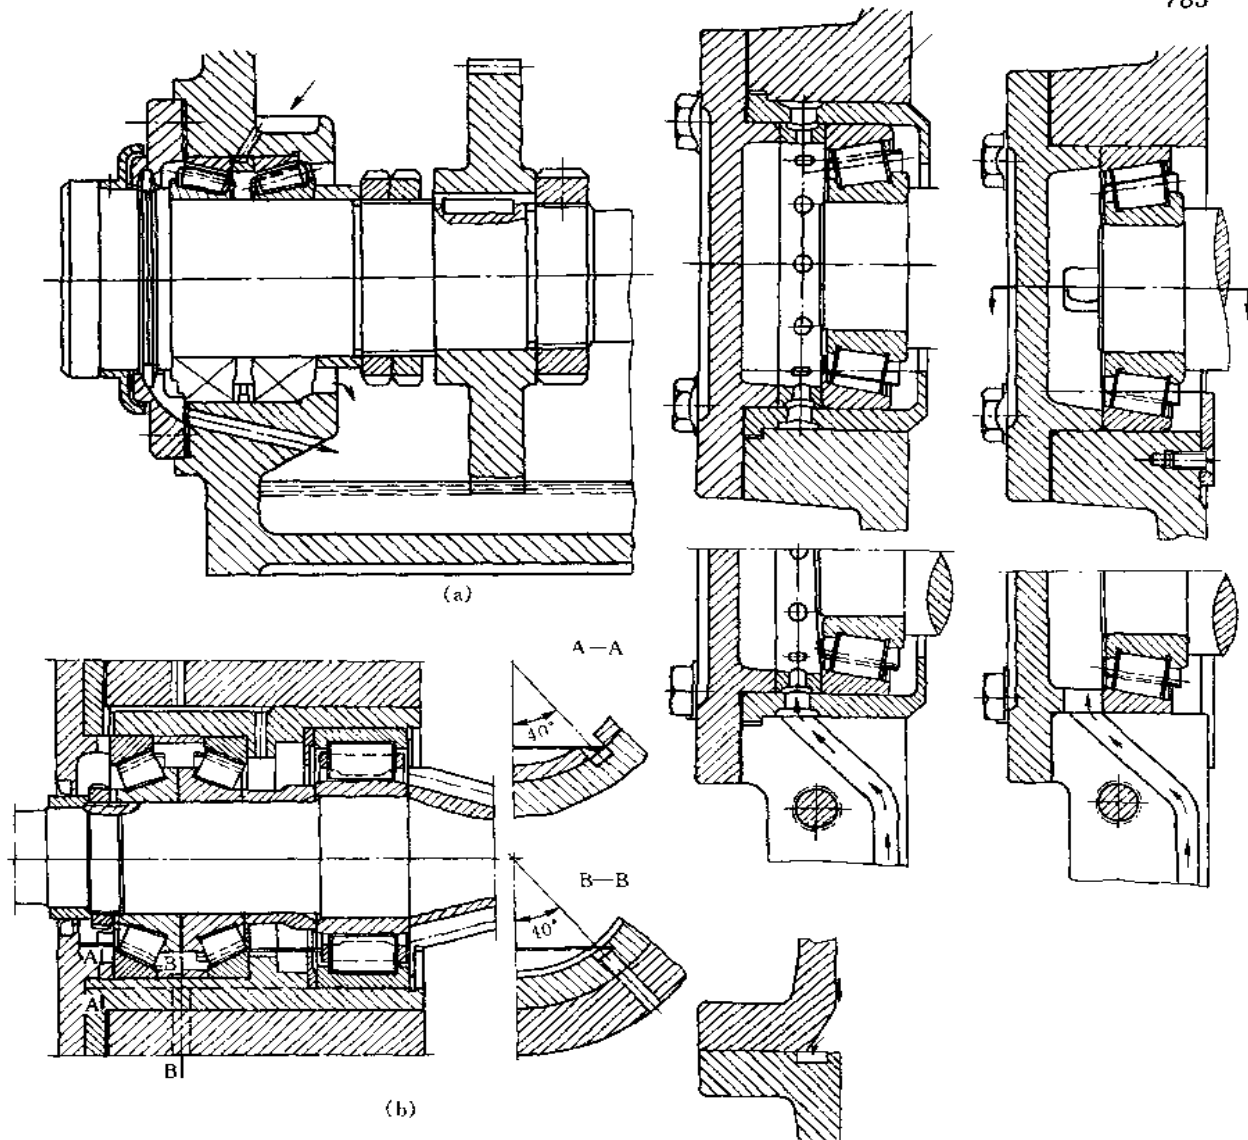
非对称轴承和齿轮轴装置的循环润滑
